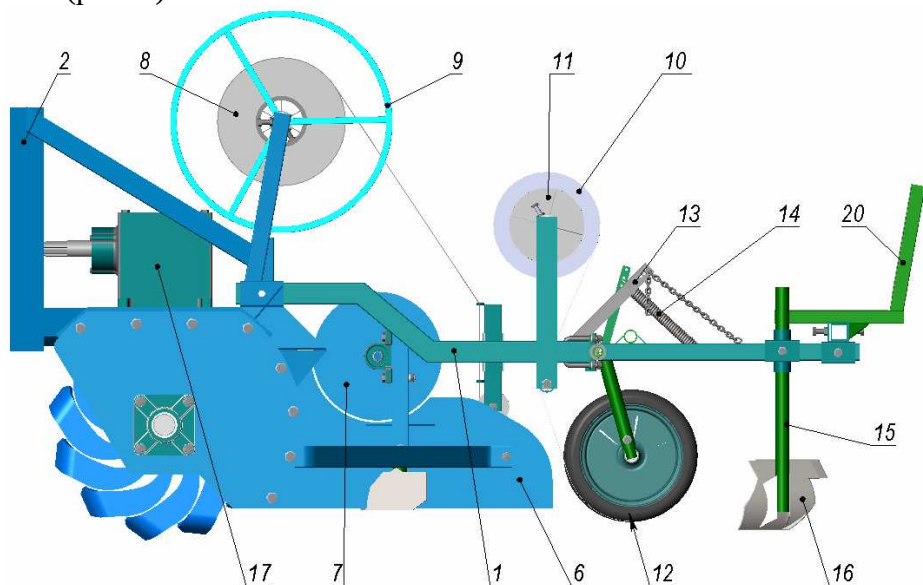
Принципиальная (конструктивно-технологическая) схема устройства для формирования места посадки клубники: 1 – рама; 2 – трехточечная навеска; 3 – фрезерный барабан; 4 – нож правого направления; 5 – нож левого направления; 6 – грядкообразующий кожух; 7 – прикатывающий барабан; 8 – капельная лента; 9 – держак; 10 – мульчирующая пленка; 11 – фиксатор; 12 – придавливающее колесо; 13 – рычаг; 14 – пружина; 15 – загортач; 16 – отвал; 17 – редуктор; 18 – звездочки; 19 – цепная передача; 20 – сиденье
